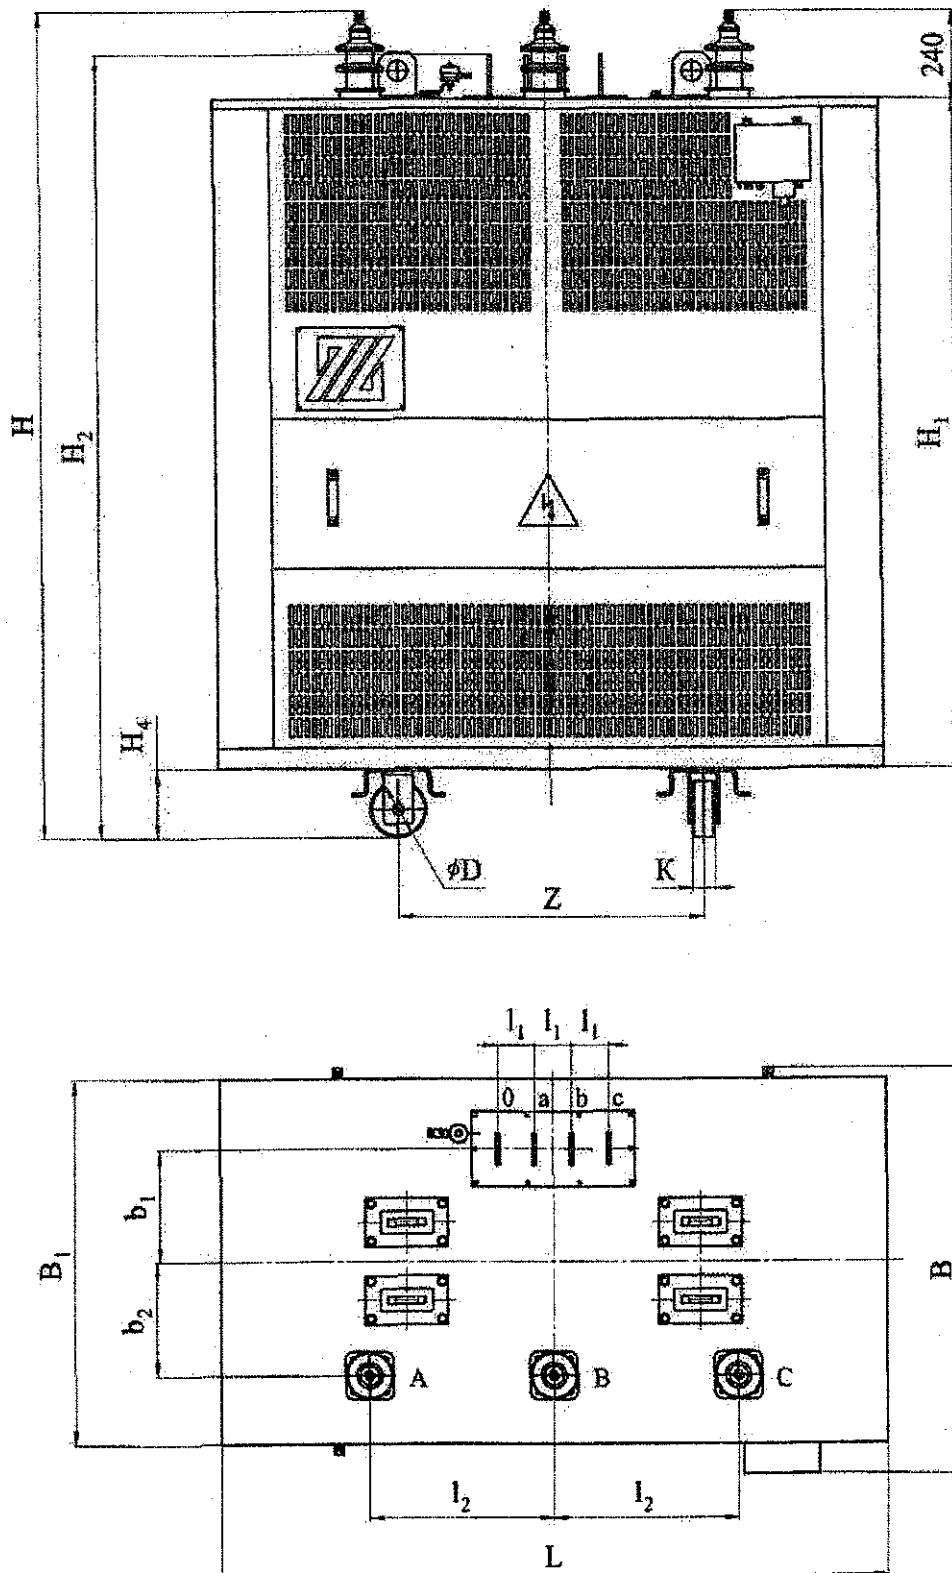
Общий вид и габаритно - установочные размеры трансформаторов серии ТСЗ мощностью 100-2500 кВ·А с расположением вводов на крышке
